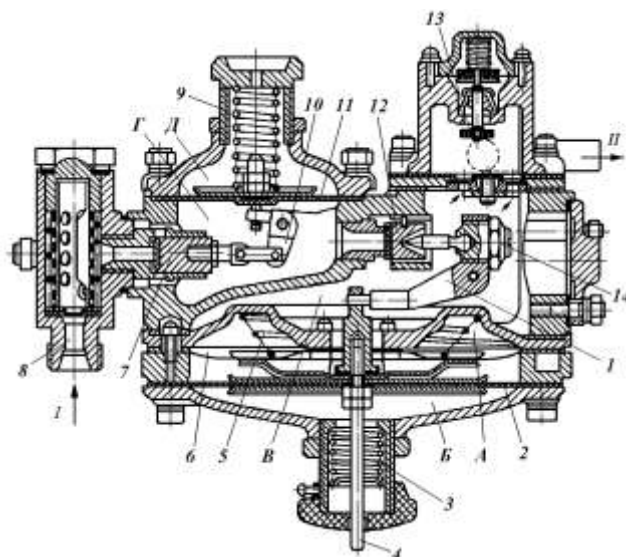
Двухступенчатый газовый редуктор низкого давления
